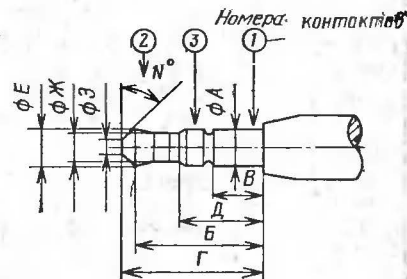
Концентрический соединитель диаметром 3,5 и 2,6 (вилки)
